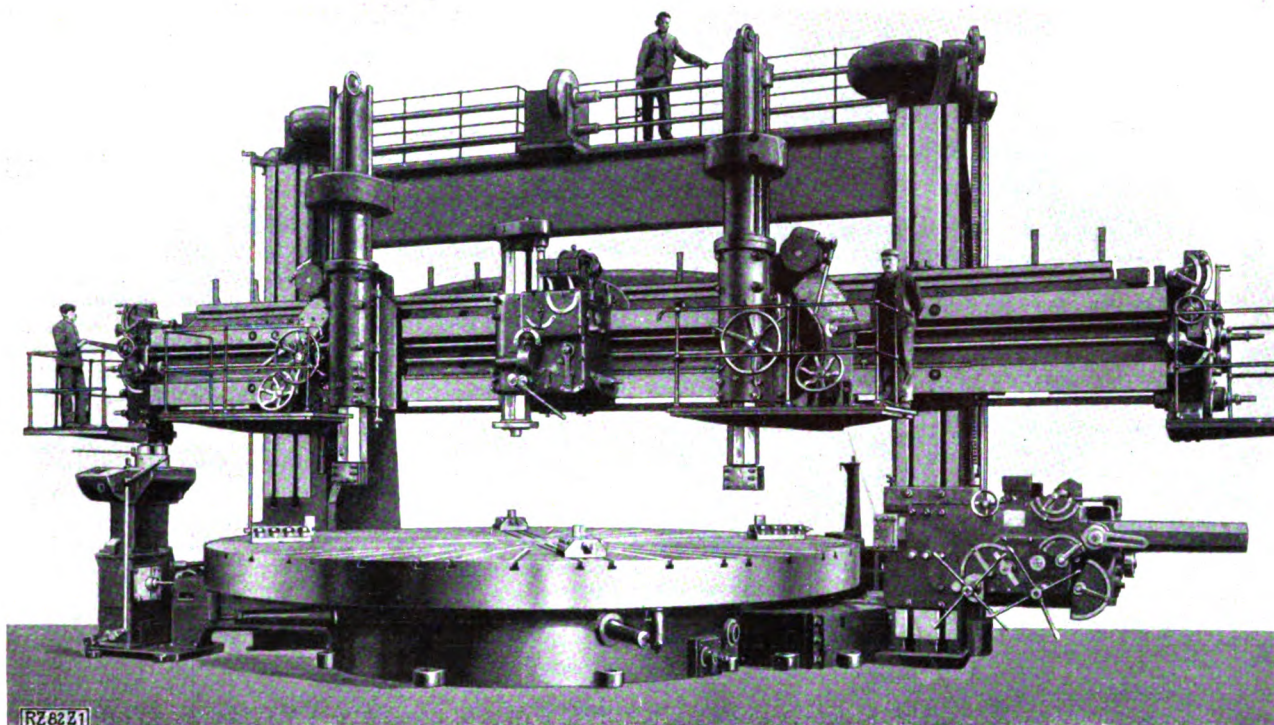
Riesen-Karusselldrehbank der Maschinenfabrik Schieß, Düsseldorf, für 8000 mm Drehdurchmesser mit einer Planscheibe von 7600 mm, Fräs- und Bohrsupport sowie Einrichtung für Stoßarbeiten.
